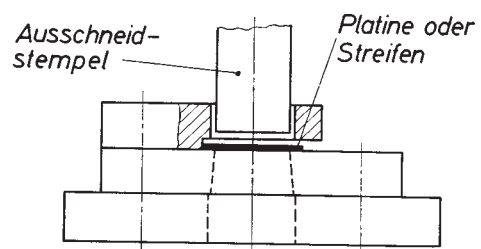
Einverfahrens-Schneidwerkzeug, z. B. Ausschneidwerkzeuge
